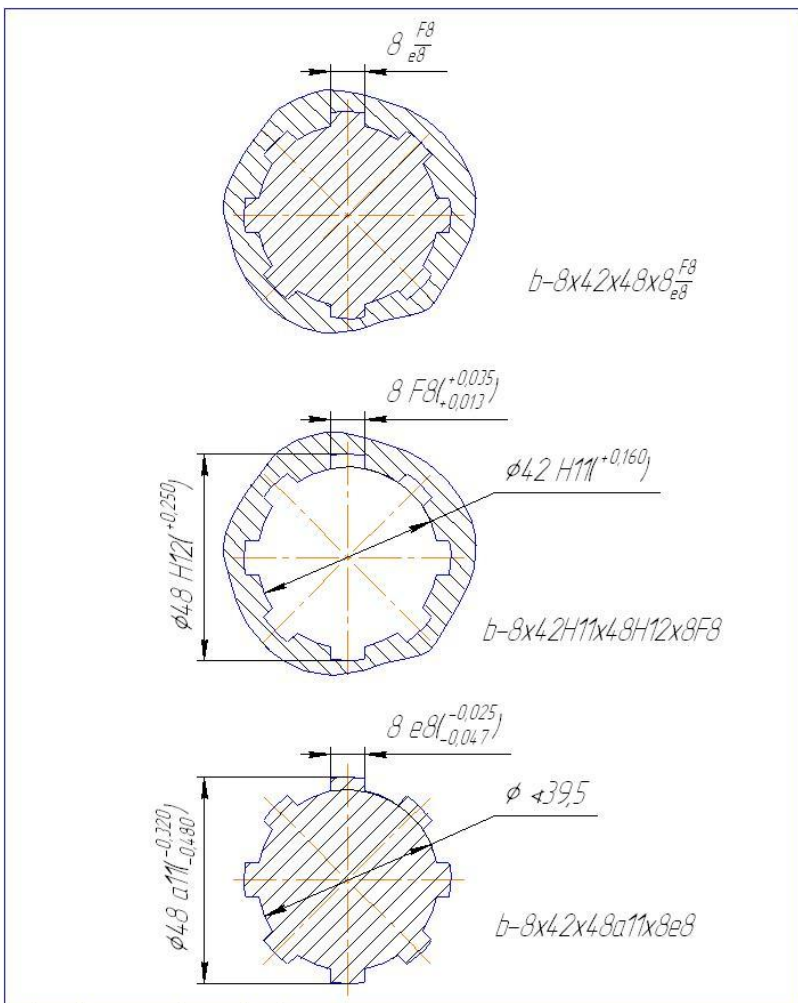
Схеми розміщення полів допусків деталей шлицевого з'єднання
